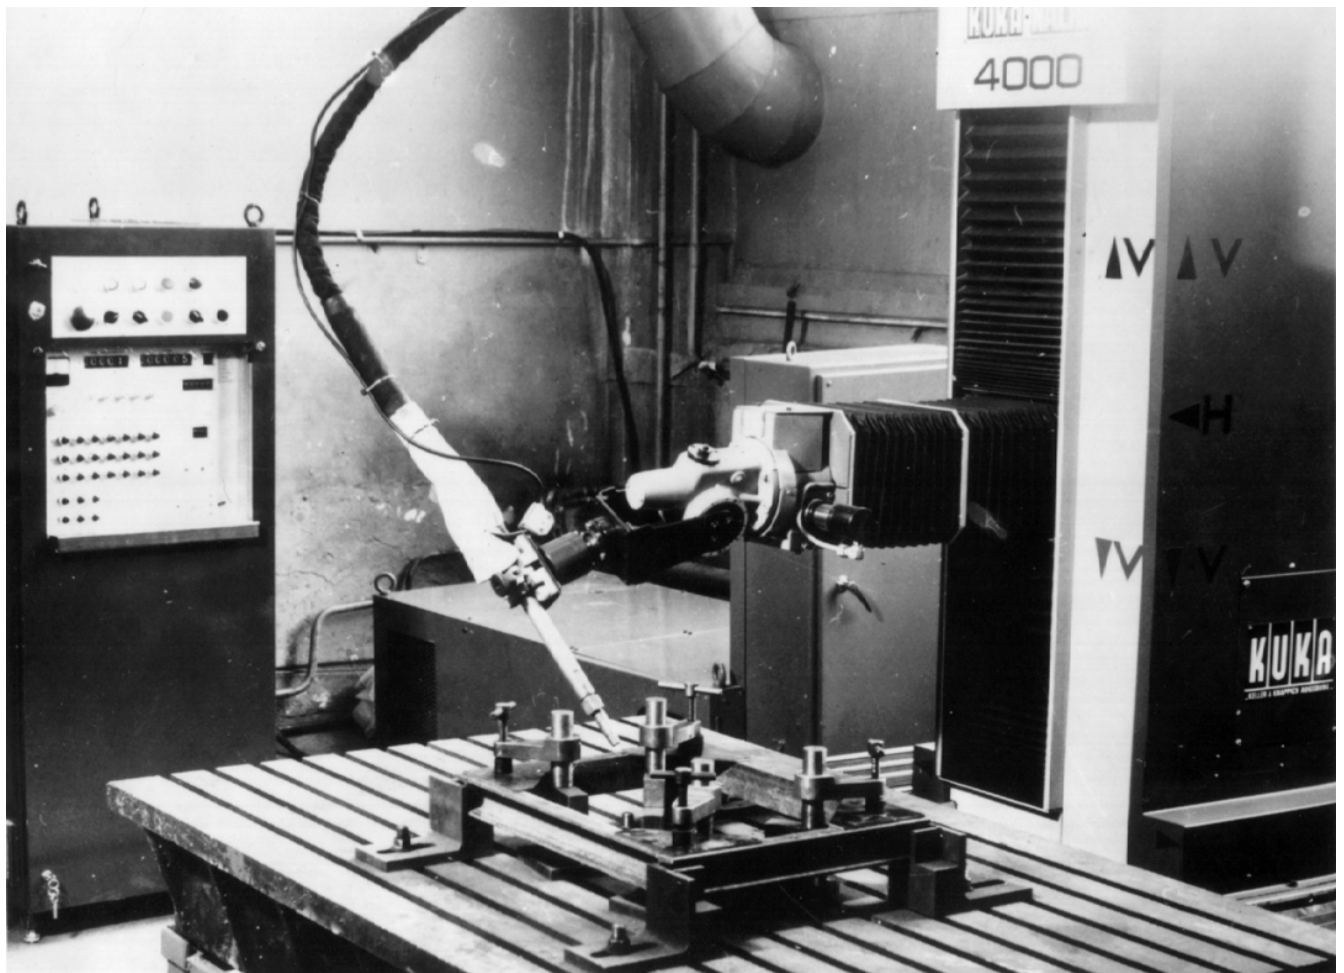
Электрический промышленный робот для дуговой сварки с непрерывным программным управлением фирмы КУКА
